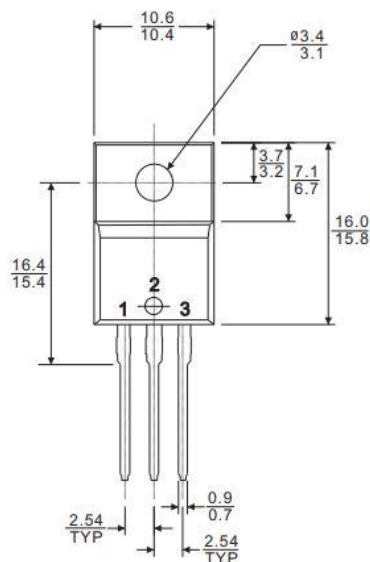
Габаритні розміри транзистора 2SA183
